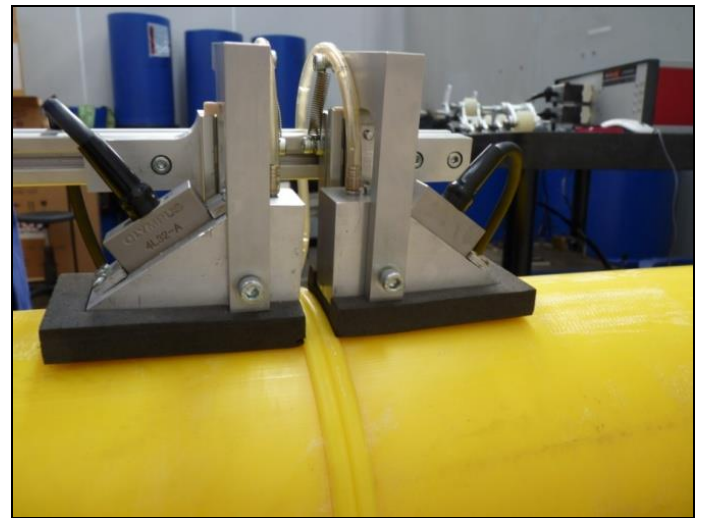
CUÑAS DE AGUA UTILIZADAS PARA INSPECCIONAR SOLDADURAS BF
